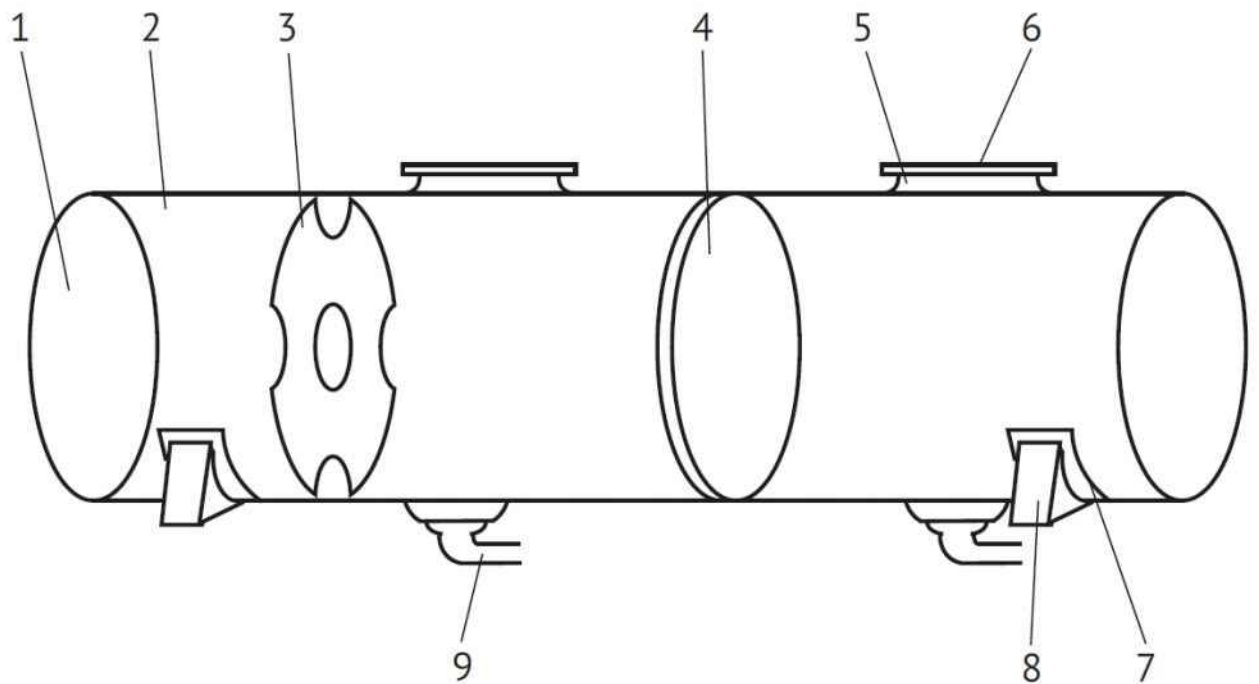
Загальна будова цистерни для перевезення наливних небезпечних вантажів: 1 - днище; 2 - обичайка; 3 - хвилеріз; 4 - перегородка; 5 - горловина; 6 - кришка горловини; 7 - накладка; 8 - опора; 9 - внутрішній запірний клапан і зливний (заливний) патрубок
